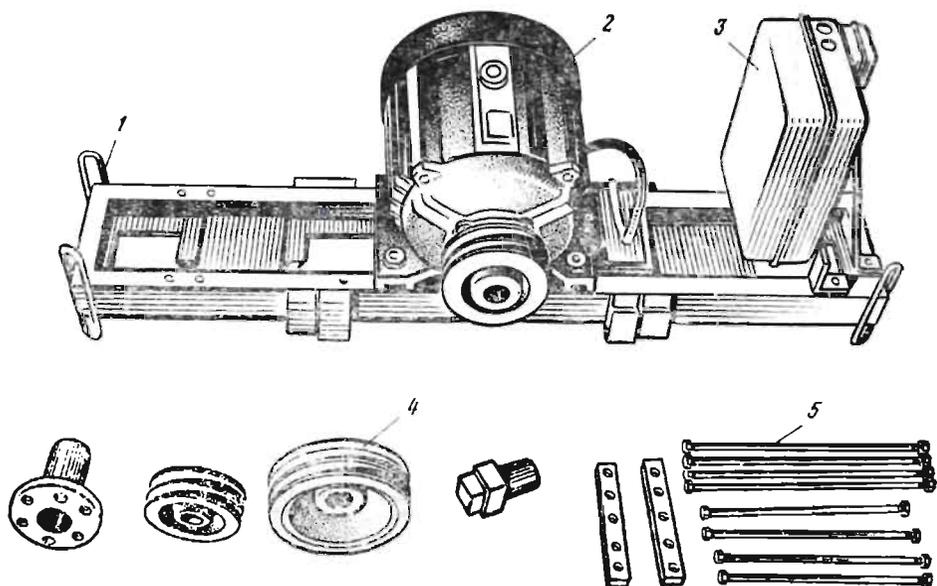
Приспособление для обкатки коробок передач и ведущих мостов тракторов:
